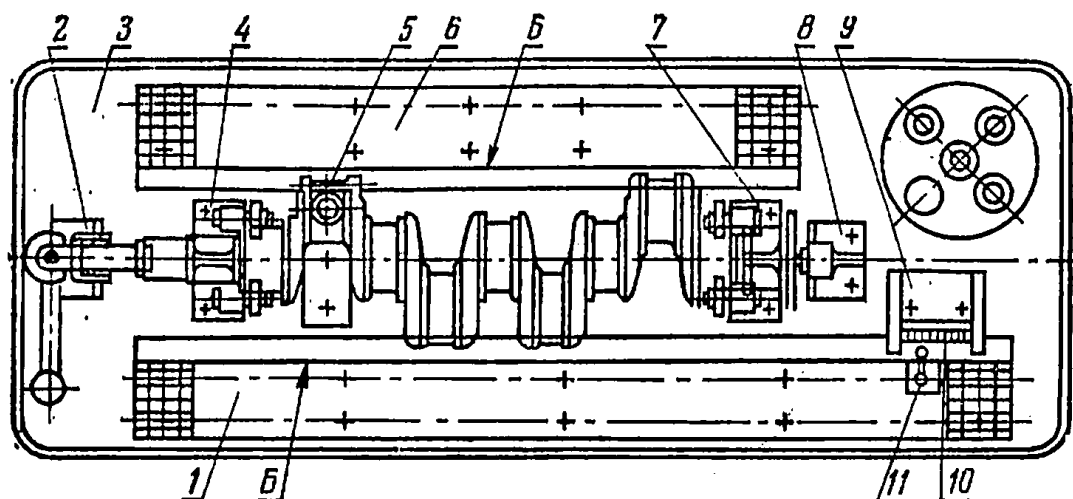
Схема приспособления для контроля коленчатого вала:
